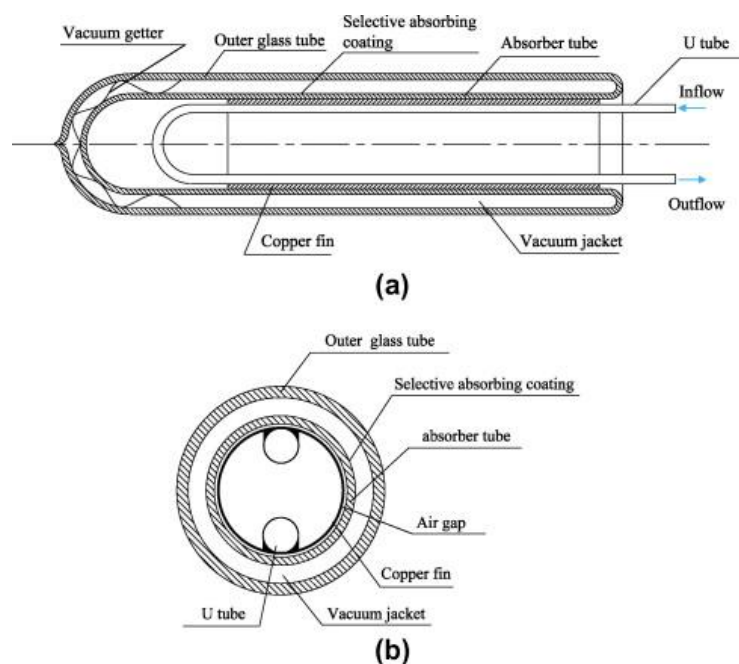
a) Vue en coupe et b) section d'un tube sous vide en U [34]
